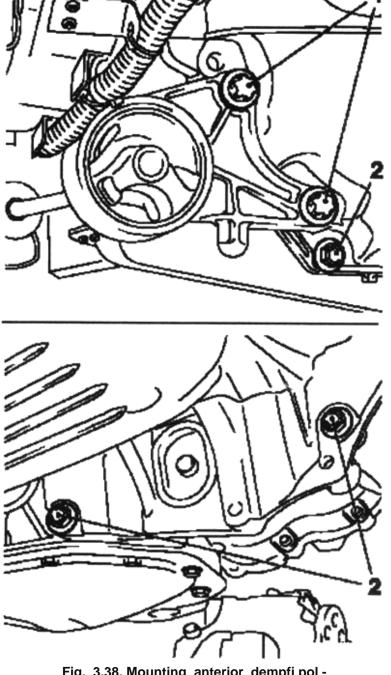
Mounting anterior dempfi polblock Engine:
